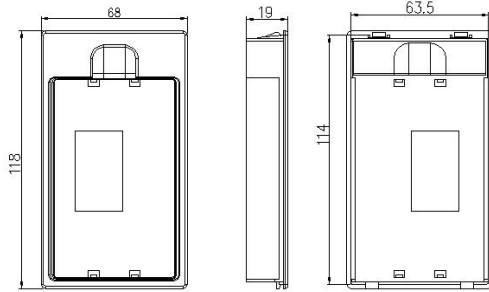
键盘托安装开孔尺寸 63.5*114 (mm)
